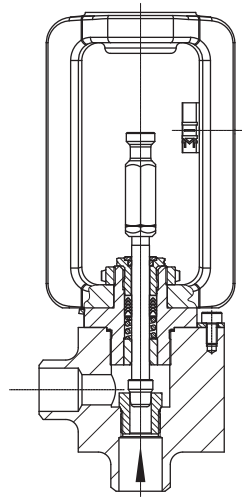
· Vanne haute pression type 3252 à passage équerre avec embouts à souder
